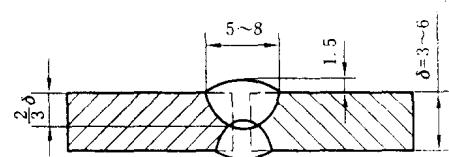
I型坡口对接焊缝的外形尺寸
